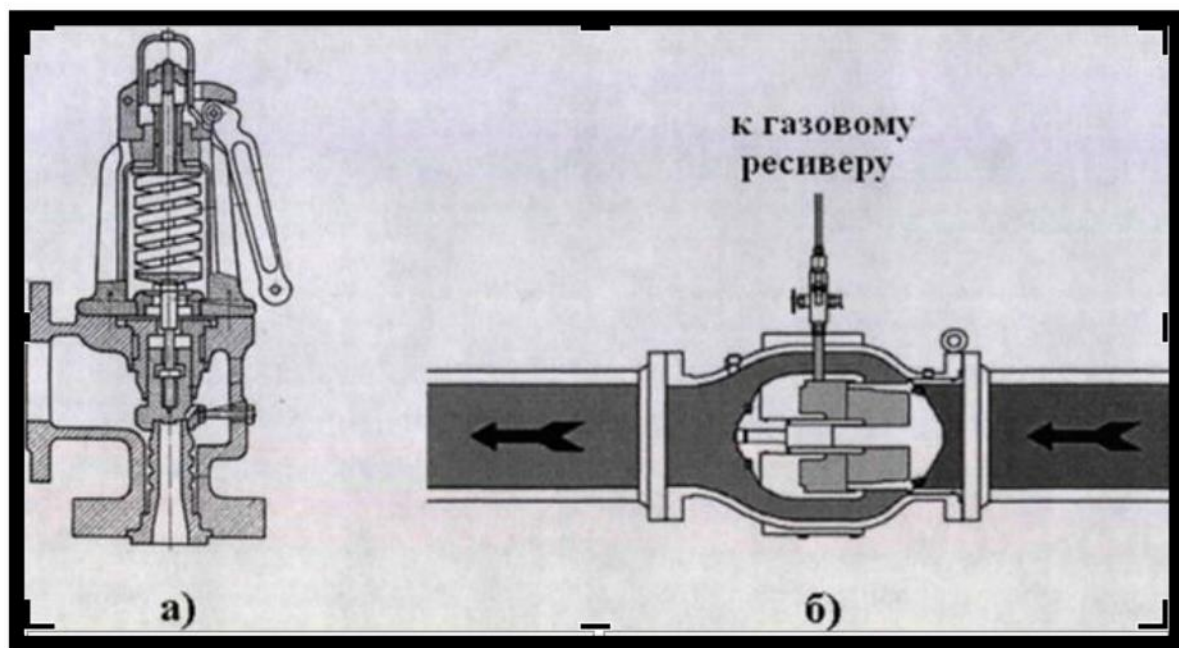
Предохранительный клапан с газовым ресивером:
